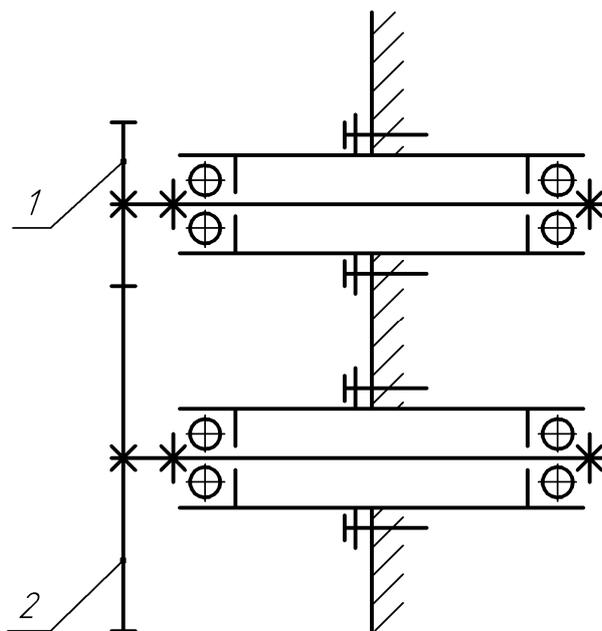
Зубчатая передача с консольным расположением колёс.
